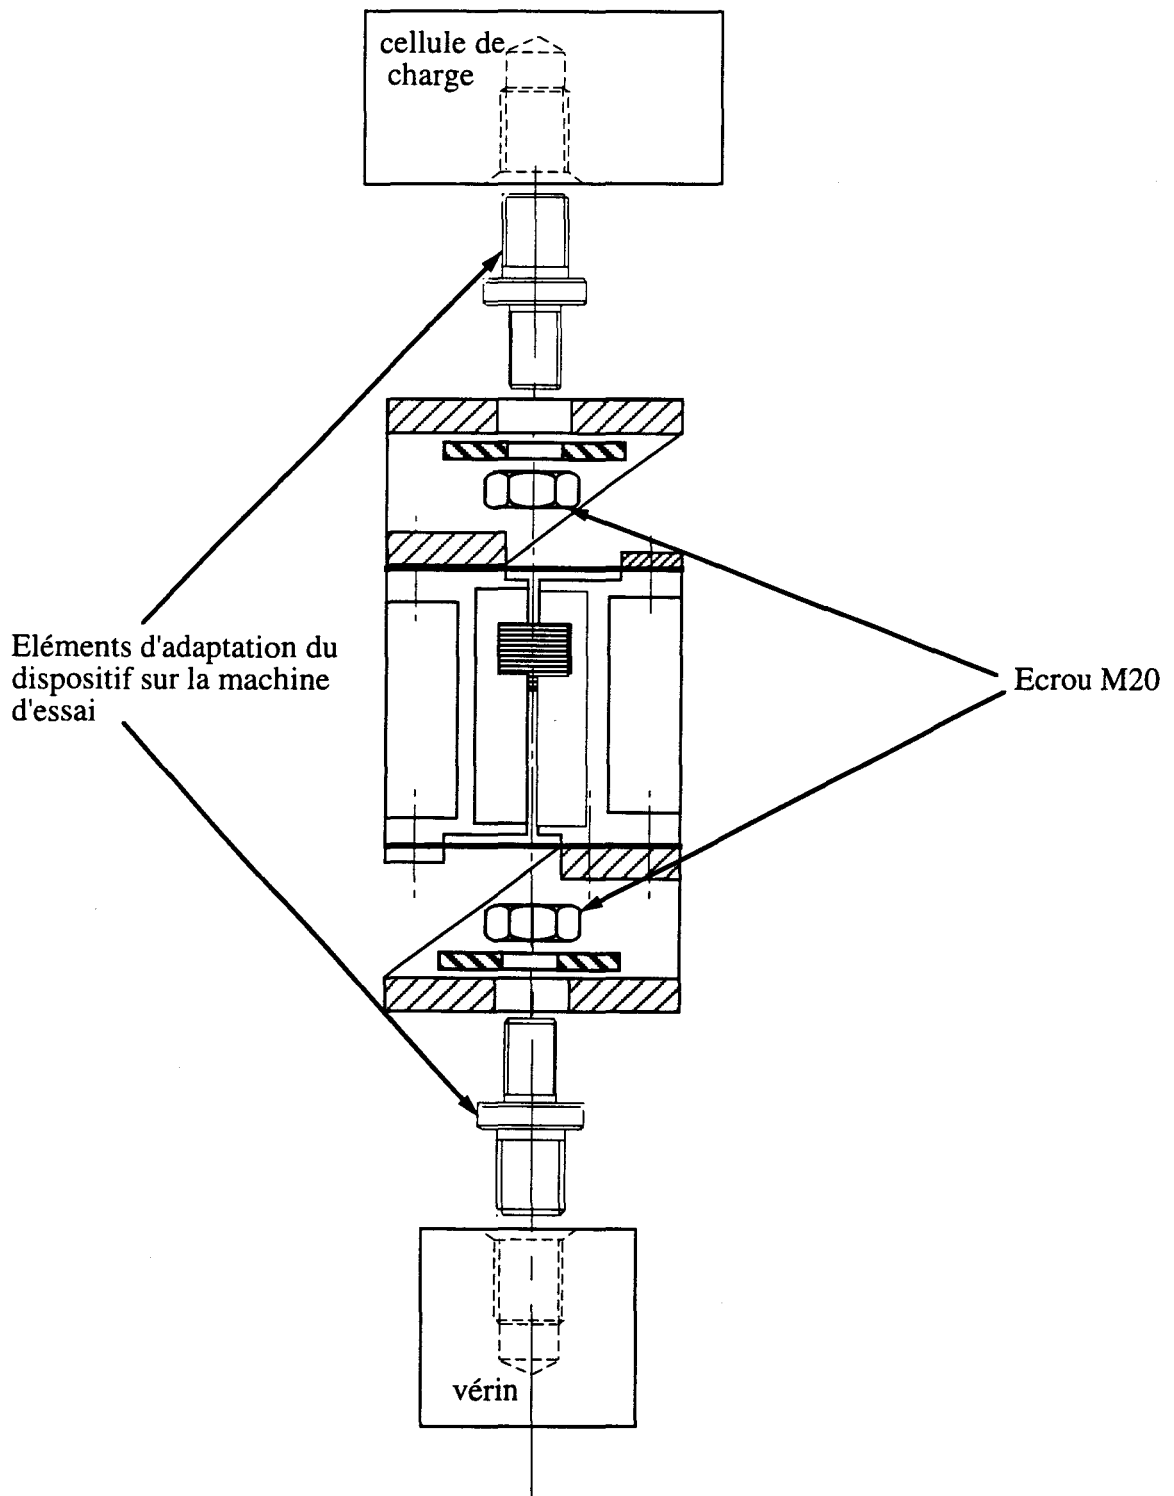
pièces d'adaptation du montage sur la machine d'essai ESH (EC Lille)
